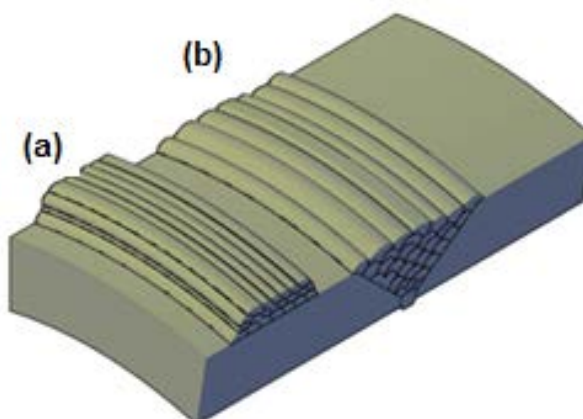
Aplicação da técnica do passe de revenimento em camadas sobreposta (a) e deposição de solda na junta chanfrada (b) para mapeamento com ensaio de dureza vickers.
